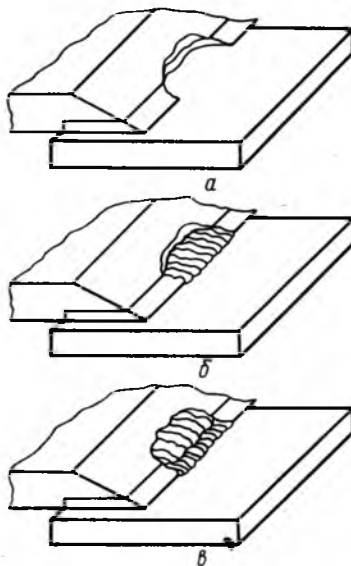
Ремонт выбоины лезвия лущильного ножа наплавлением:
